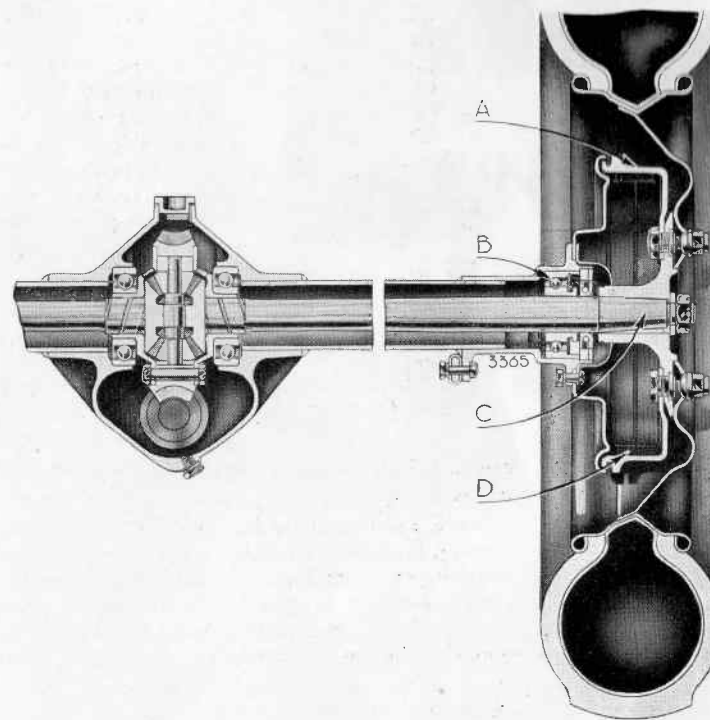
Coupe du pont arrière et vue d'un frein.
